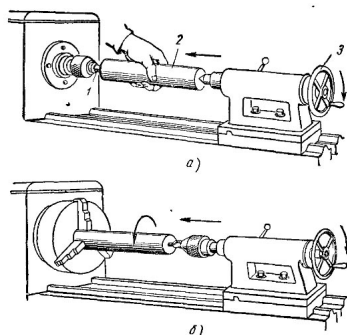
Сверление центрального отверстия комбинированным центровочным сверлом
